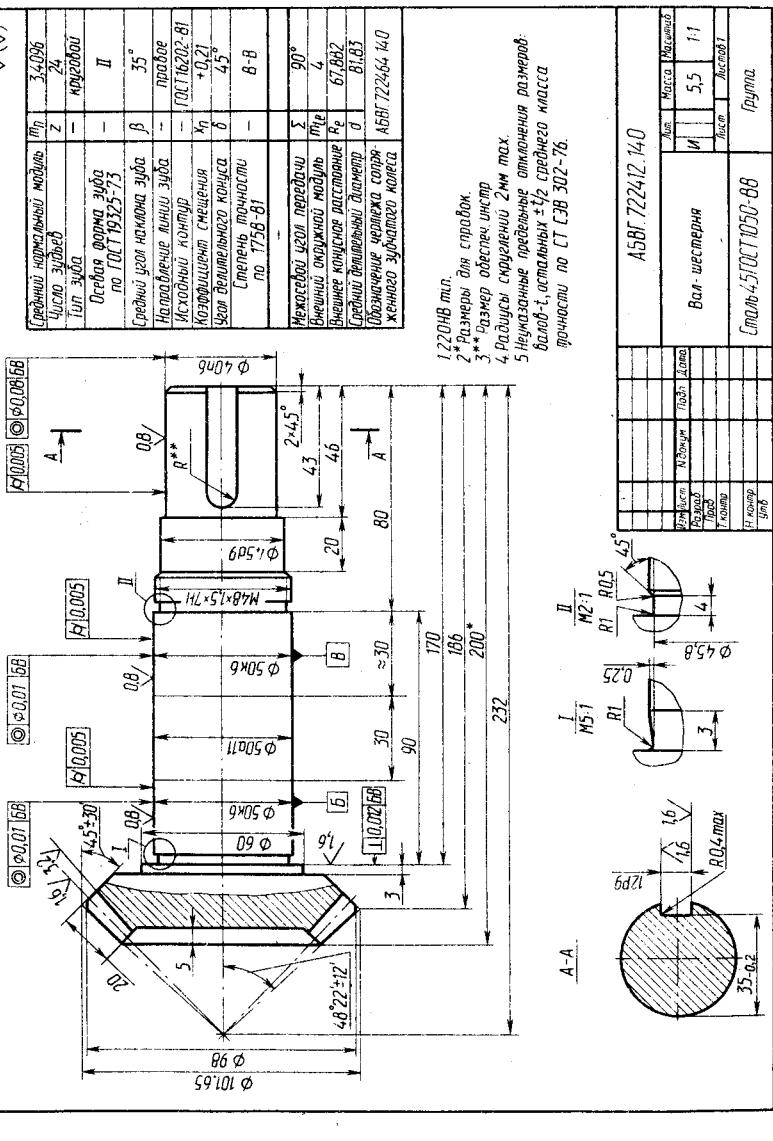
Пример рабочего чертежа вала-шестерни конической
